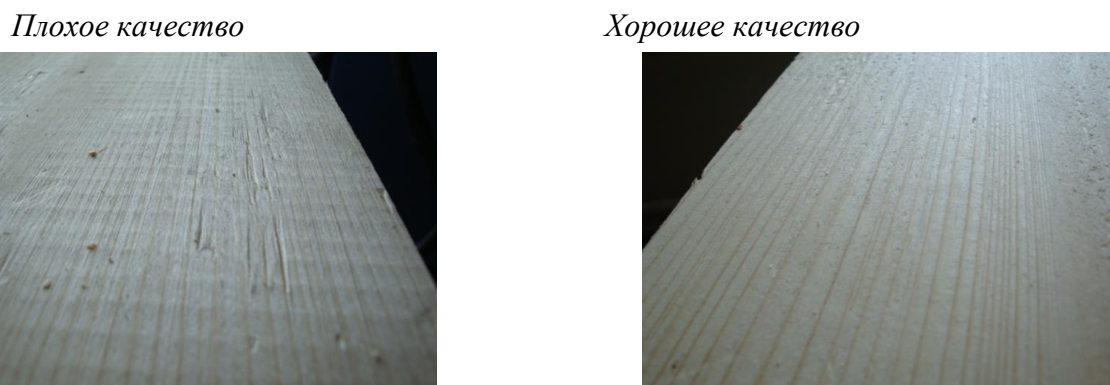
Качество обработанных поверхностей методом цилиндрического фрезерования.
